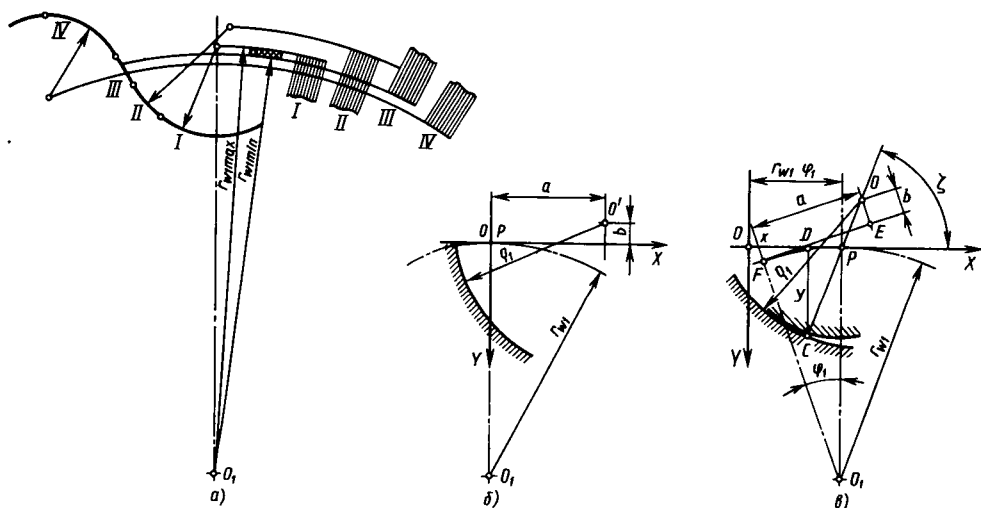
Определение положения центроиды и профиля режущей кромки червячной фрезы для обработки фасонного профиля детали
